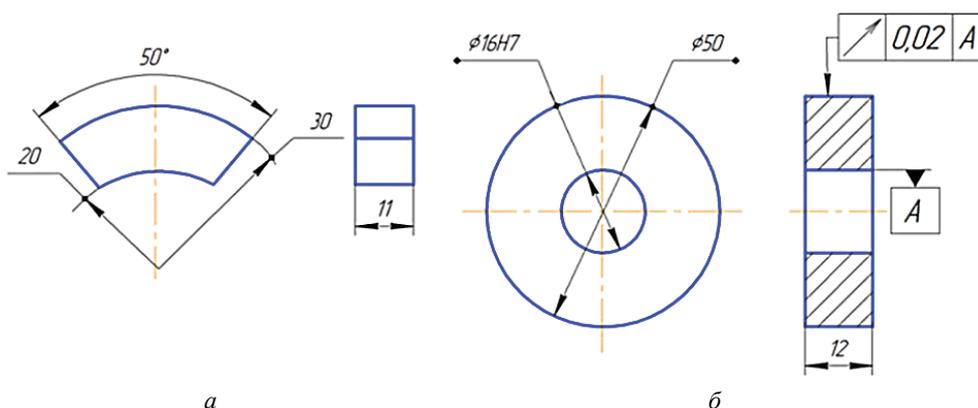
Общий вид образцов для испытаний на изнашивание:
